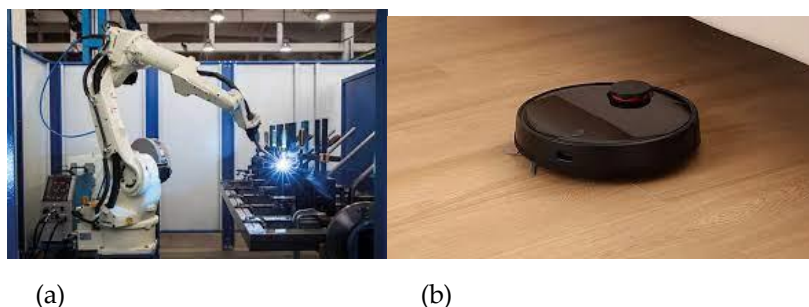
(a) Robot soldador [9]. (b) Robot aspirador [10]
